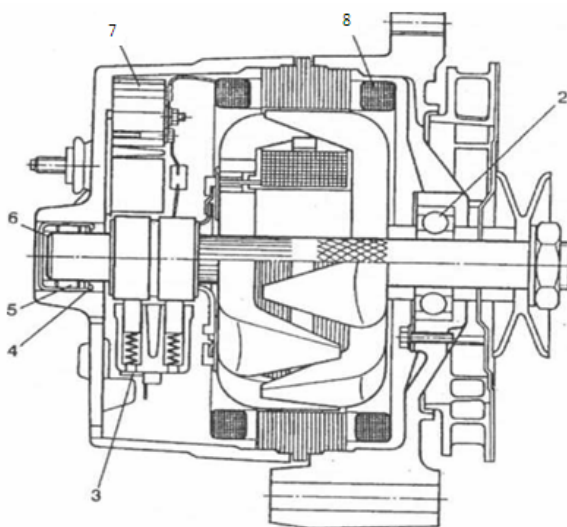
Генератор 1281-100: 1 - статор; 2 – підшипник; контактні щітки; 4- ущільнювач; 5 – втулка; 6 – вісь якоря; 7 – діодний блок; 8 – обмотки статора [12]
